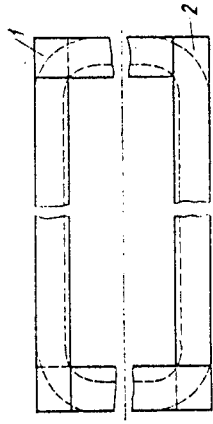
Приспособление для изолировки и рихтовки катушек
